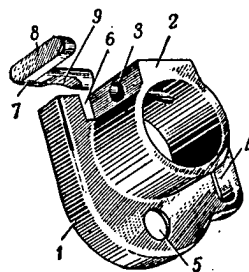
Газова камера (1-29) (общ вид и разрез):
